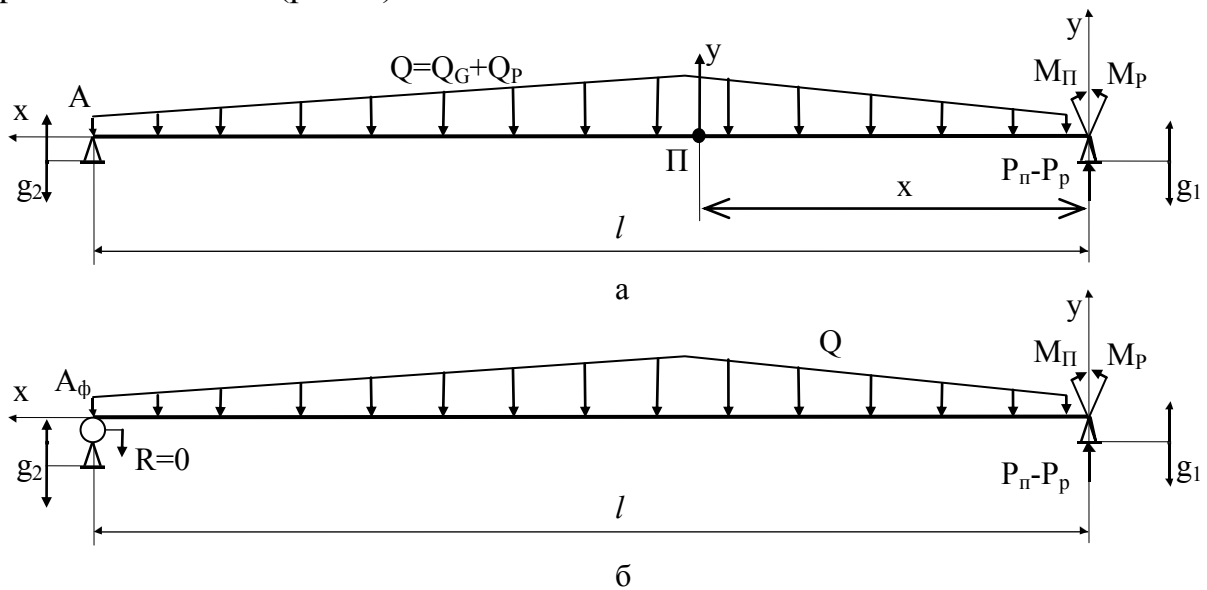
Розрахункова схема динамічної системи заготовки із врахуванням розподіленості параметрів по довжині: а-варіант підтримки заготовки з лівого краю; б-консольний варіант встановлення заготовки.
